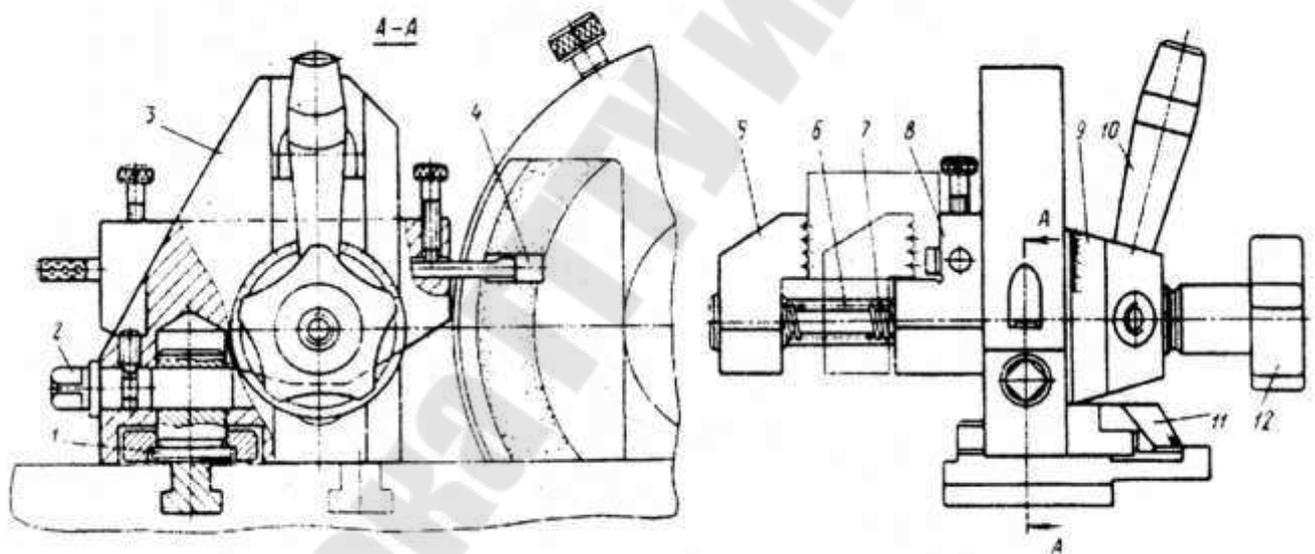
Приспособление для закрепления резцов при заточке передних поверхностей
